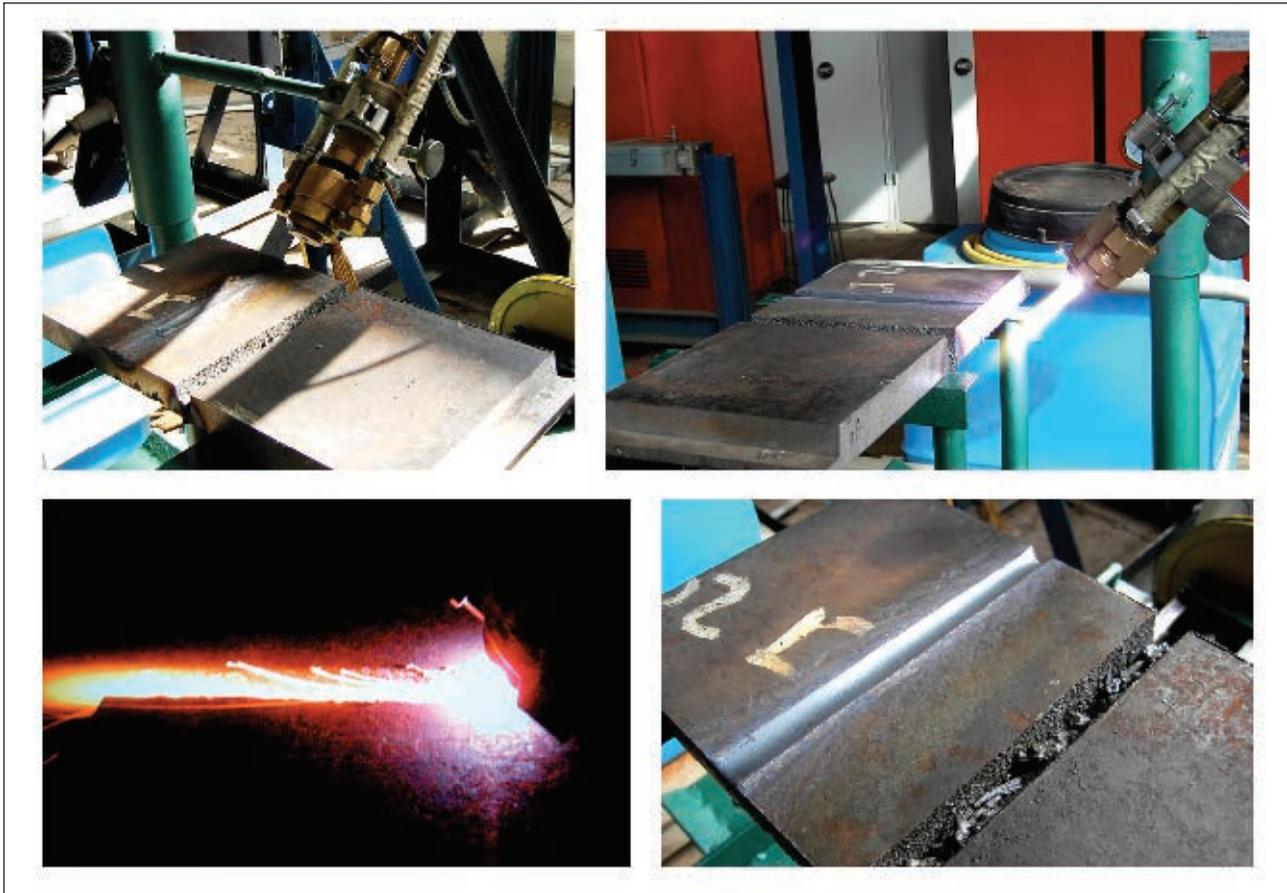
Плазменная модификация сварных соединений после контактной стыковой сварки оплавлением и удаления грата
